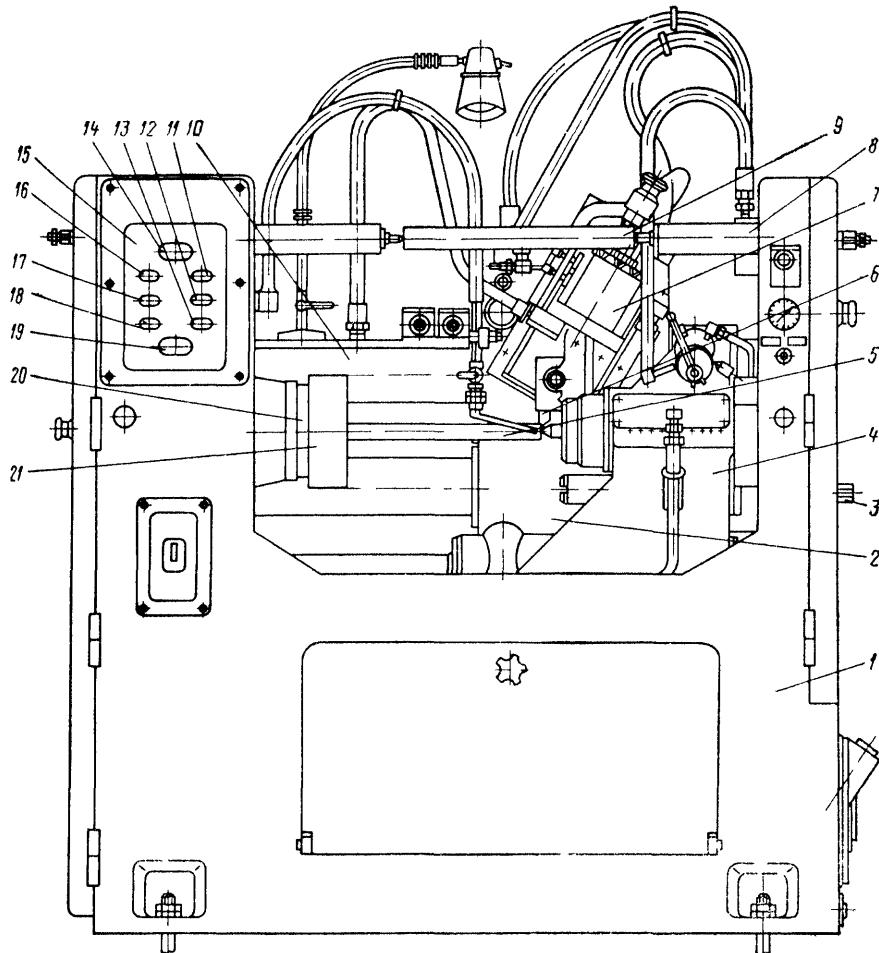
Специальный токарно-копировальный полуавтомат модели СИ-035.
